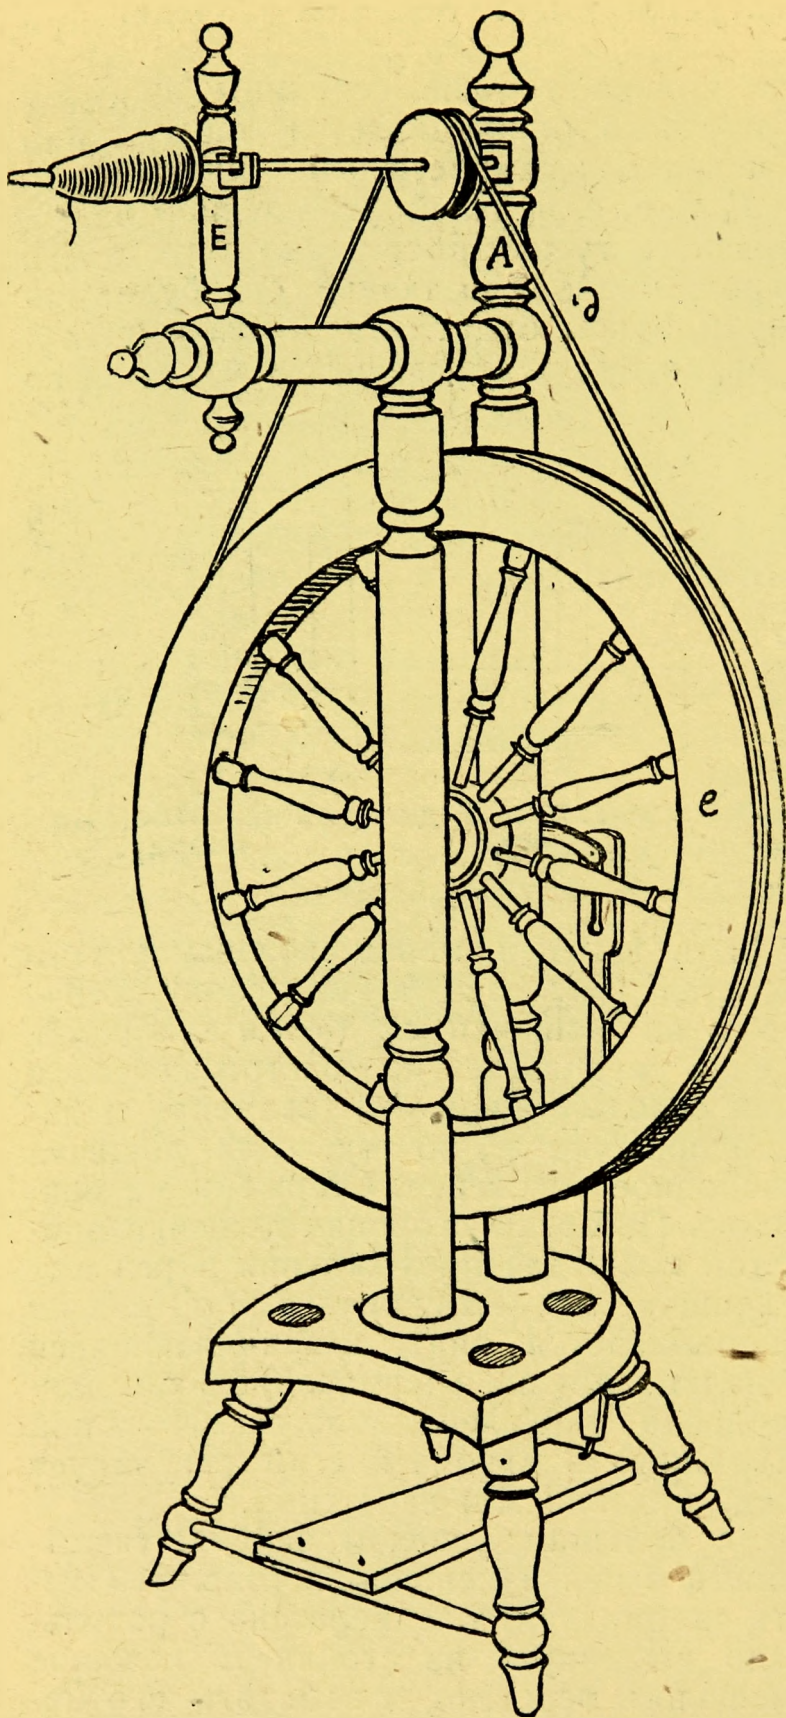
Самопрялка, приспособленная для размотки пряжи на катушки и цевки.
